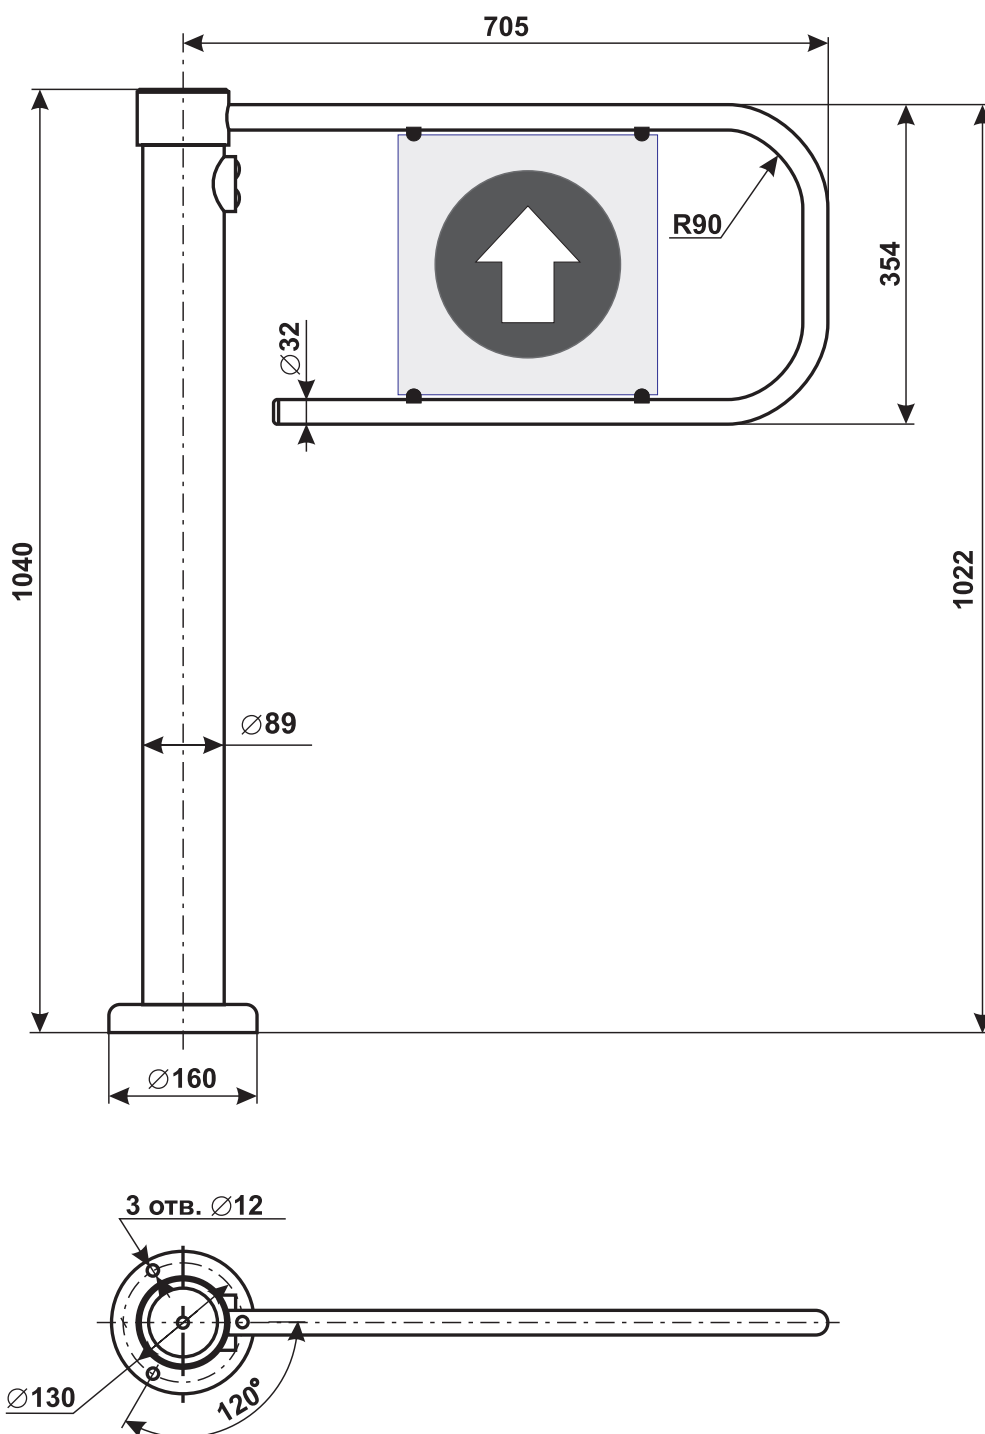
Габаритные размеры калитки PERCo-WHD-04
